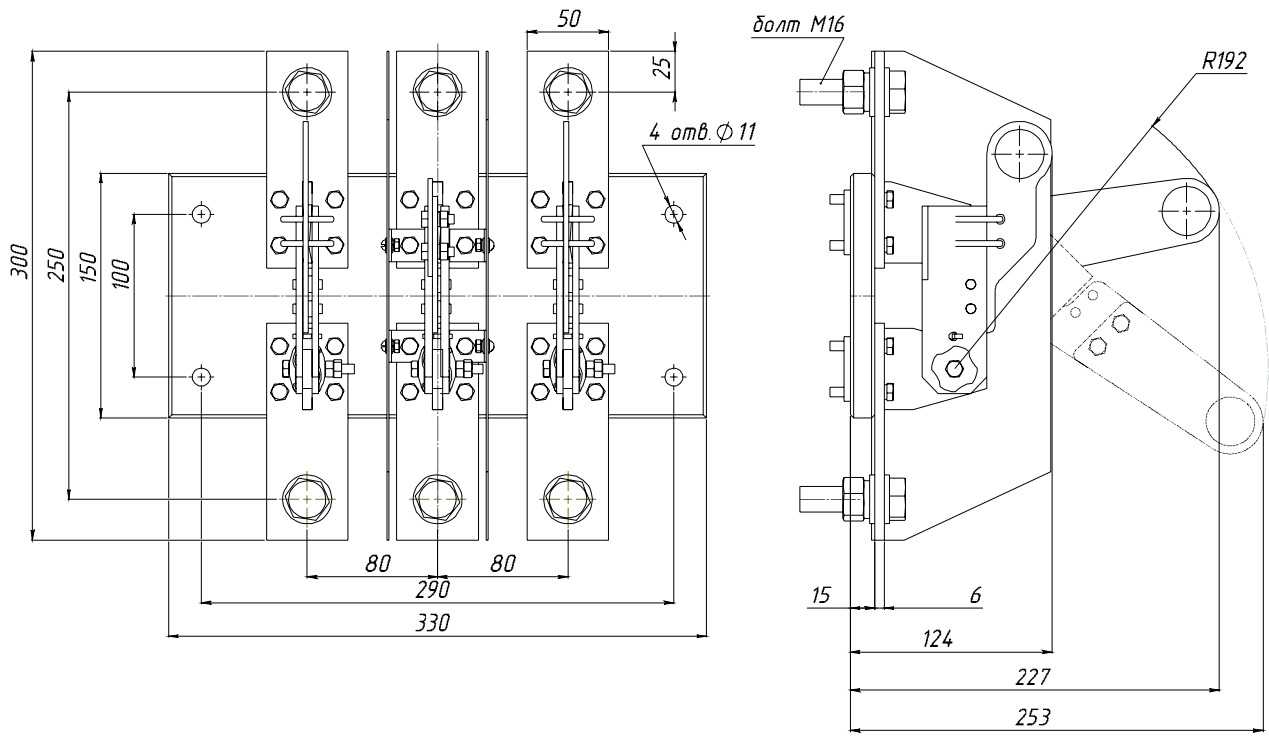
Разъединитель серии Р с полюсным оперированием штангой Р103 на номинальный ток 1000 А.
